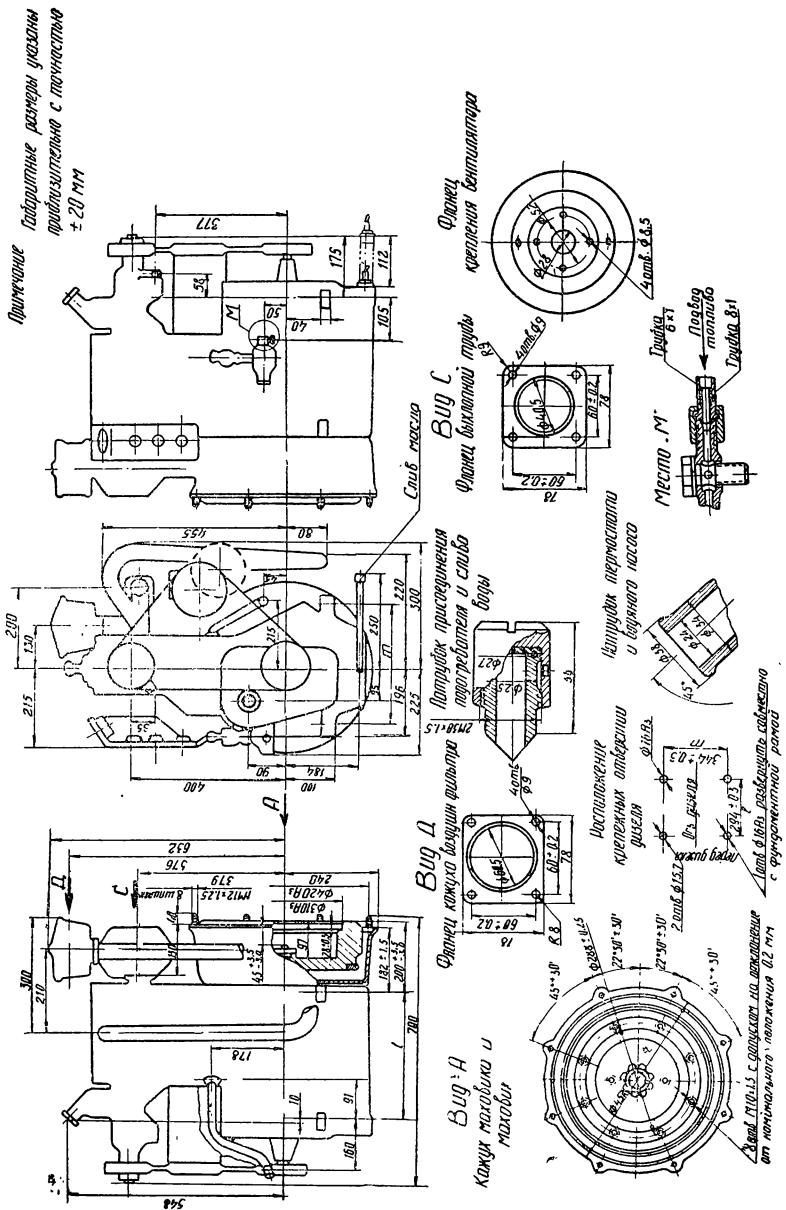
Габаритный чертеж дизеля 2 Ч 8,5/11 (1П2-6, 1П2-7).
